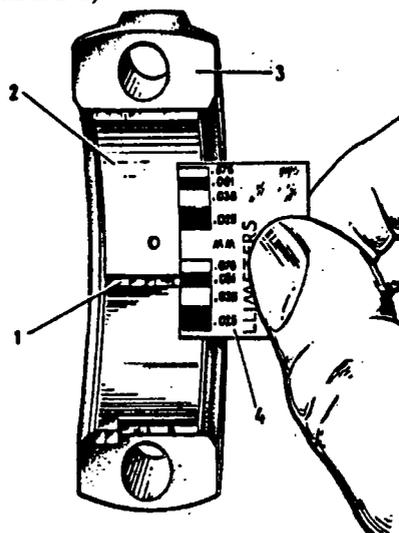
Измерение с помощью шкалы ширины калиброванной проволоки после сплюсживания: 1 - калиброванная проволока; 2 - вкладыш; 3 - крышка шатунного подшипника; 4 - шкала для калиброванной проволоки
